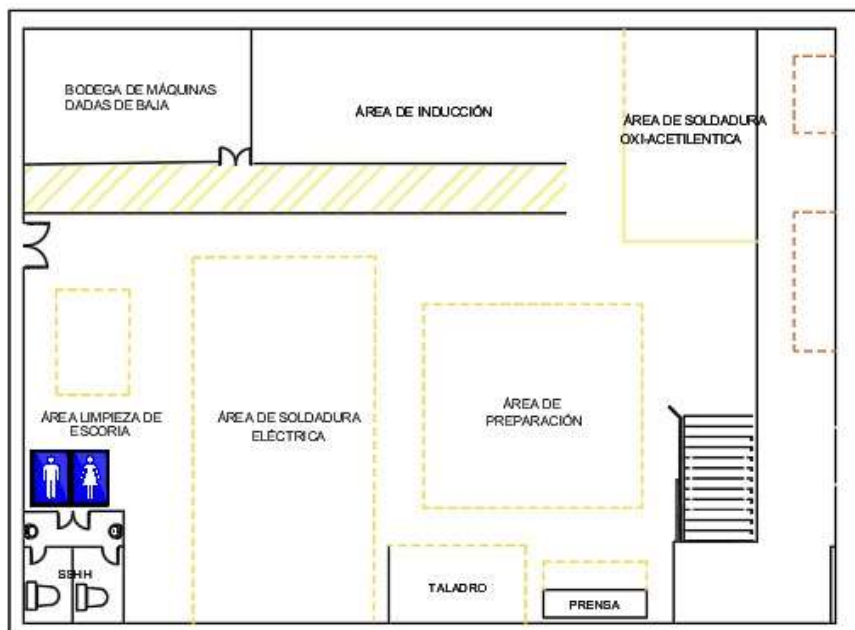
Layout- Taller de soldadura de la facultad de mecánica
